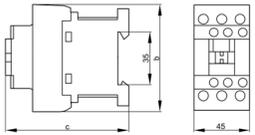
Габаритные размеры контакторов ПК-225XX- ПК-232XX
